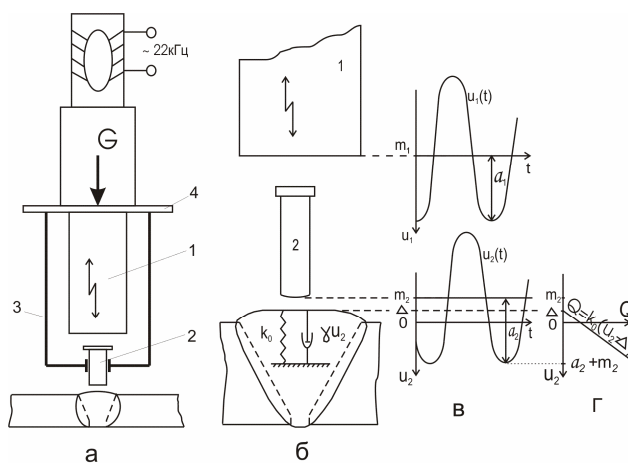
Схема ультразвукового инструмента (а); схема зоны обработки (б); развертки колебаний волновода и ударника (в); силовая характеристика контакта ударника с обрабатываемым изделием. Обозначения приведены в тексте.
